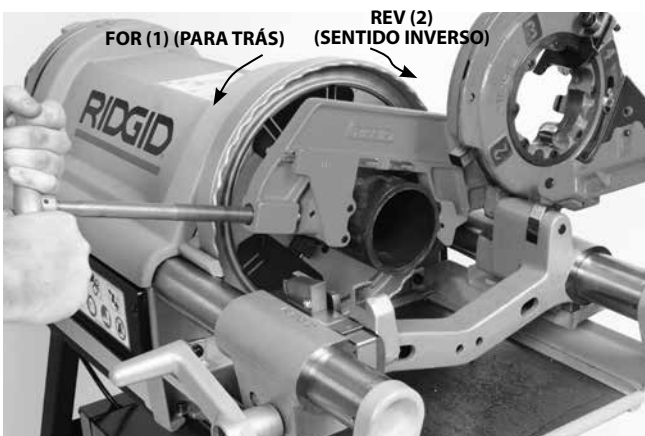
Cortar Tubo com Cortador/Rotação da Máquina 764
